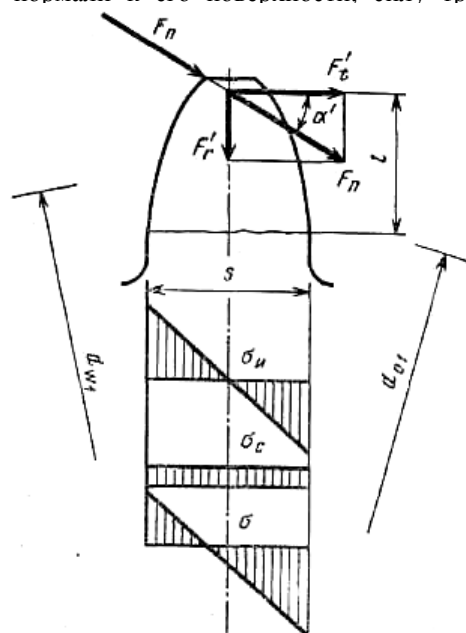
Расчётная схема нагружения зуба прямозубого цилиндрического колеса
